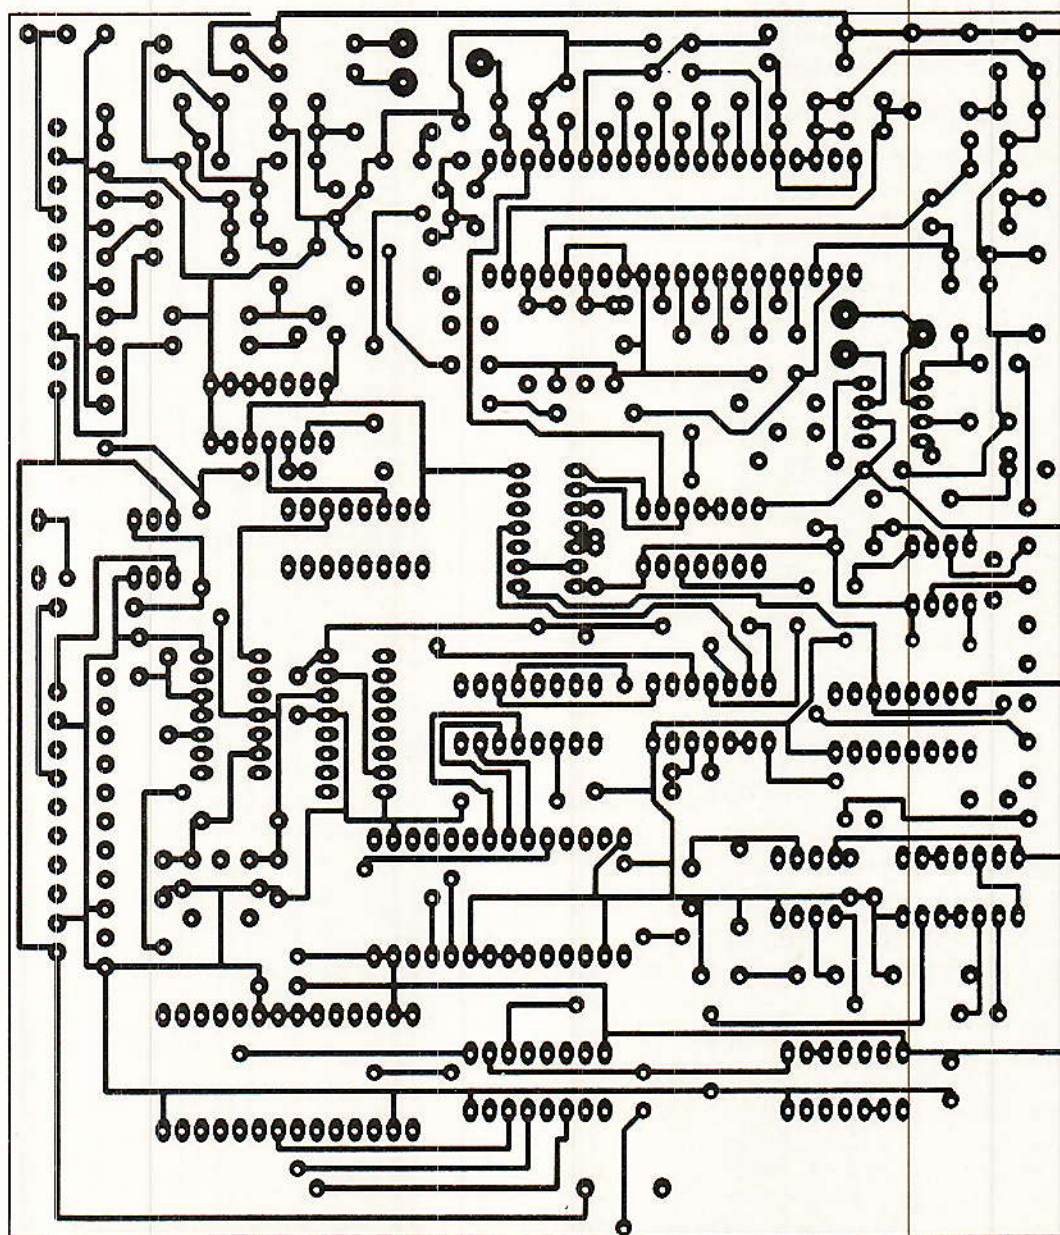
Circuit imprimé de la carte principale, côté soudures.
